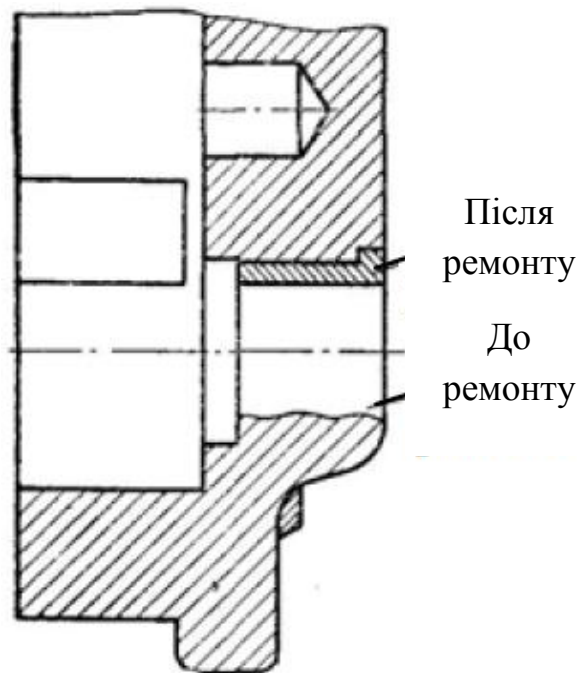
Схема установки втулки підшипника в зношеному корпусі
